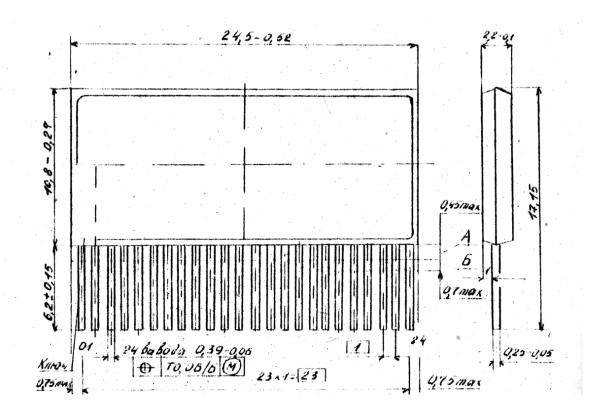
Габаритный чертеж корпуса 4192Ю.24-1
